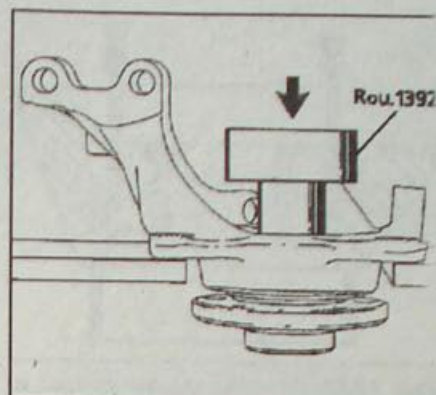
Использование приспособления Rou. 1392 для выпрессовки ступицы из поворотного кулака
